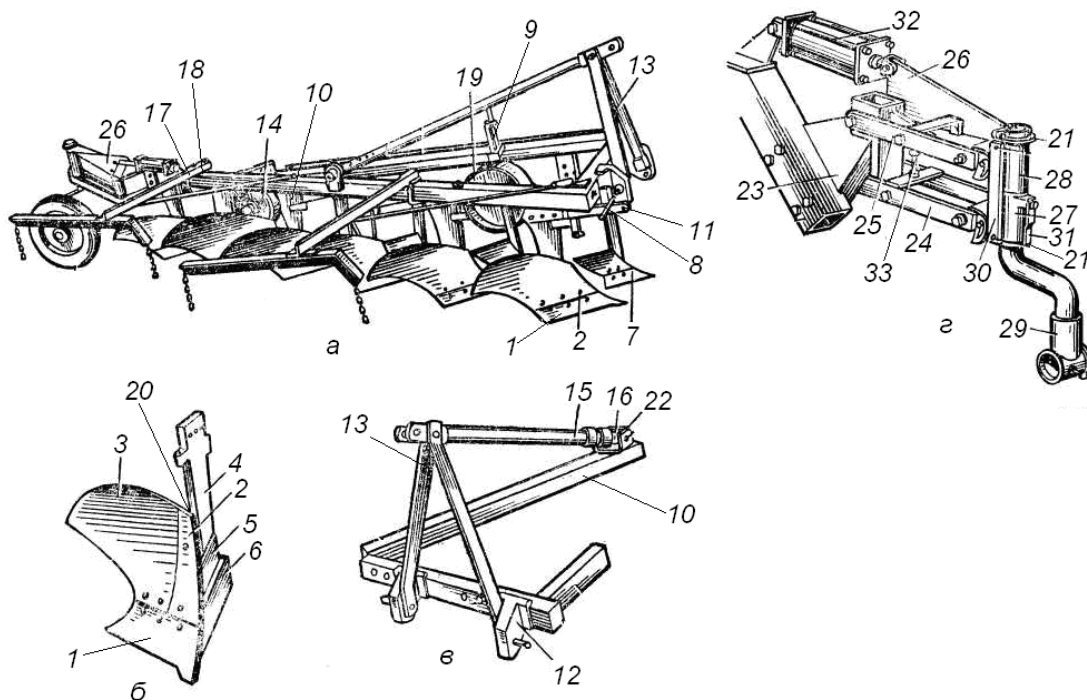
а – общий вид плуга; б – корпус плуга; в – навесное устройство; г – механизм заднего колеса.
